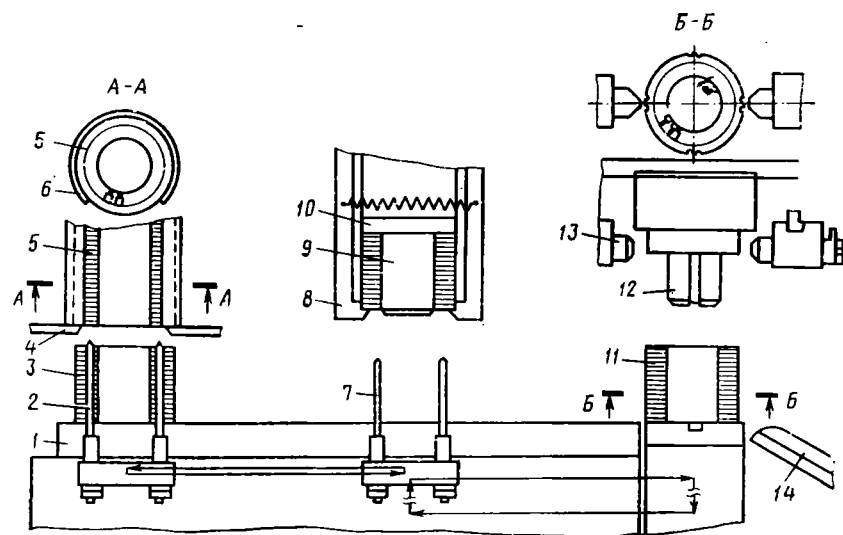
Схема рабочих органов установки ВСС-5 для автоматической сборки сердечников статора или ротора:
